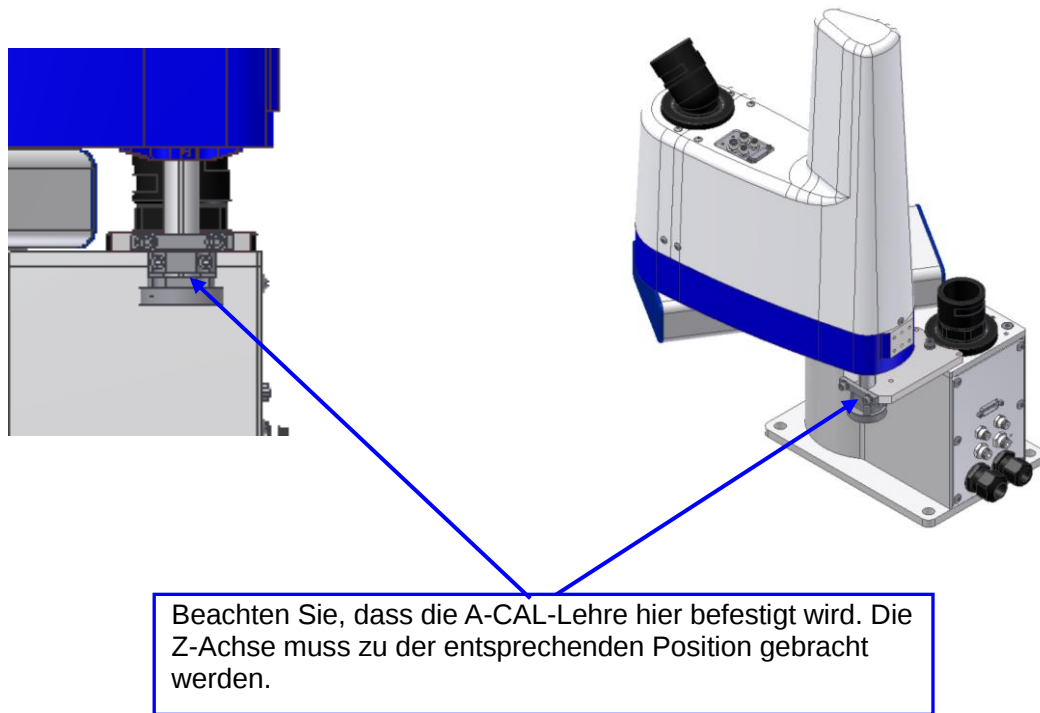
Befestigungsposition der A-CAL-Lehre
